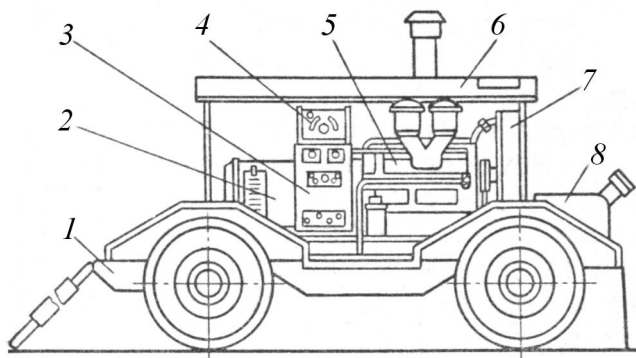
Загальний вигляд зварювального агрегату АСДП-500:
